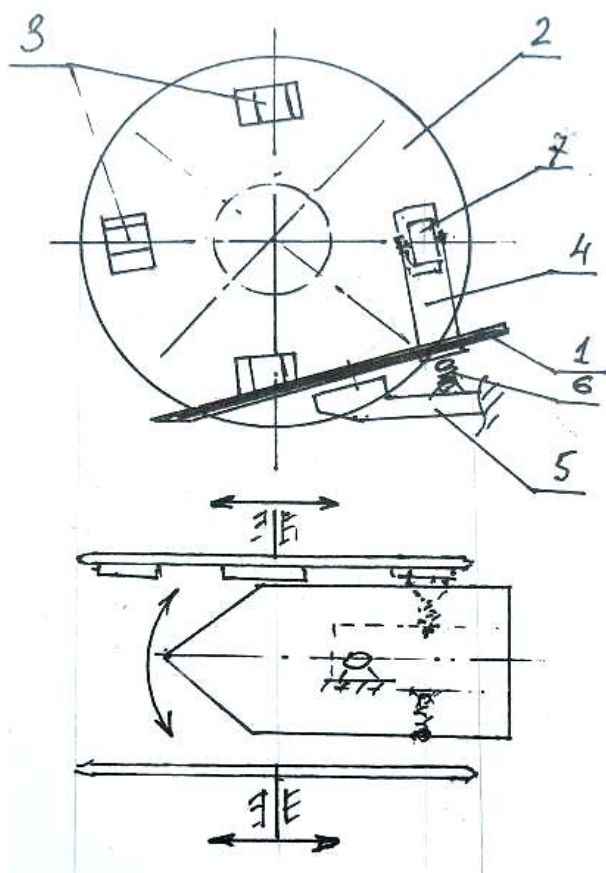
Схема предлагаемой конструкции подкапывающего органа
